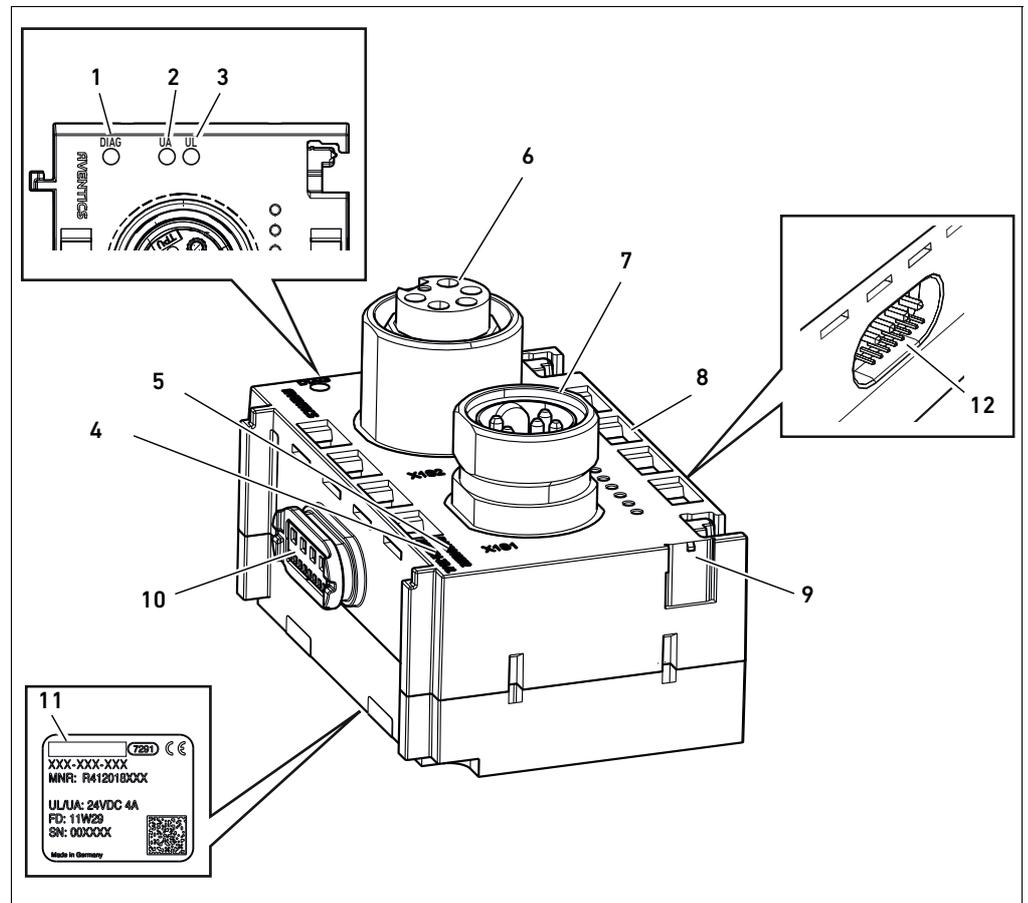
Enhetsöversikt Powermoduler med 7/8"-anslutning
